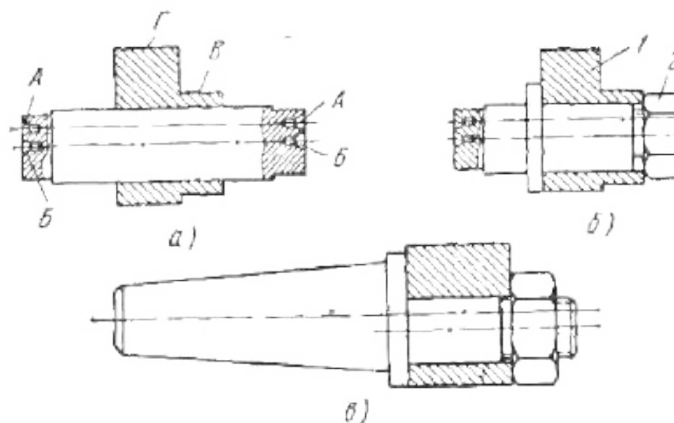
Оправки для обточування ексцентрикових деталей:
